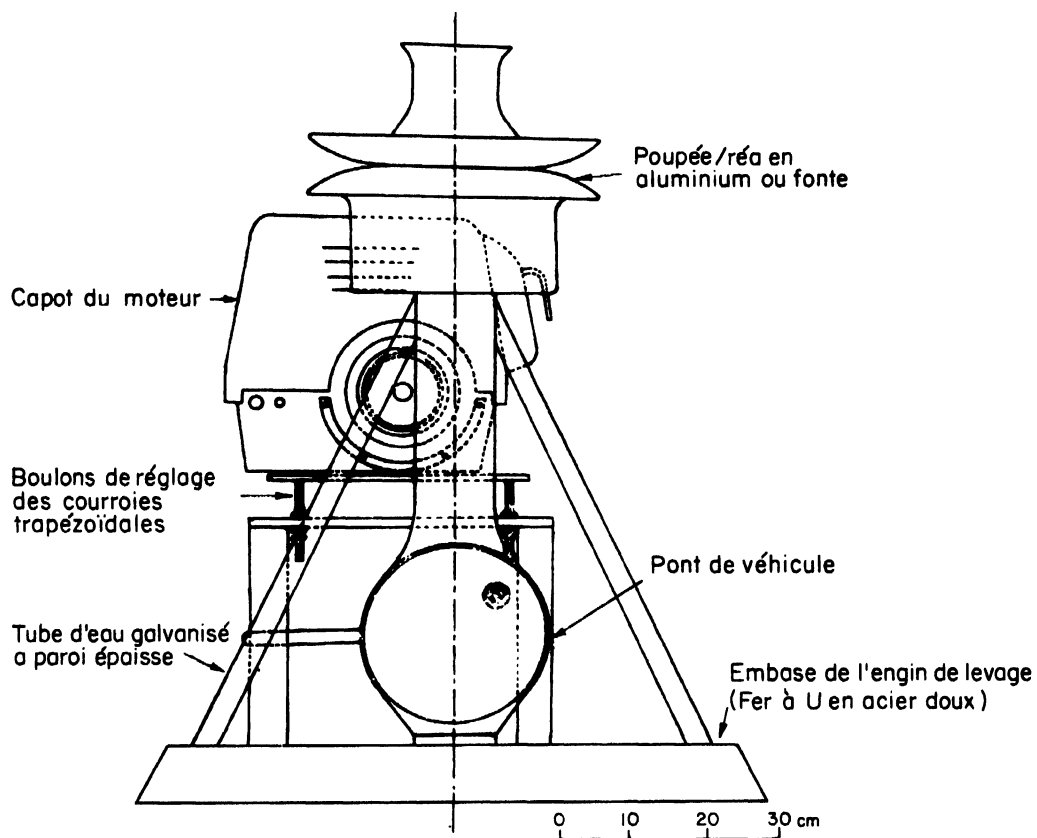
VUE EN BOUT DE L'ENGIN
